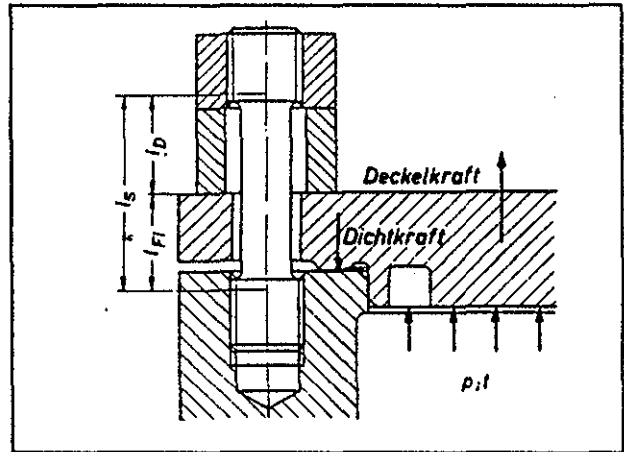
Deckelverschluß mit Flanschschrauben [5]
